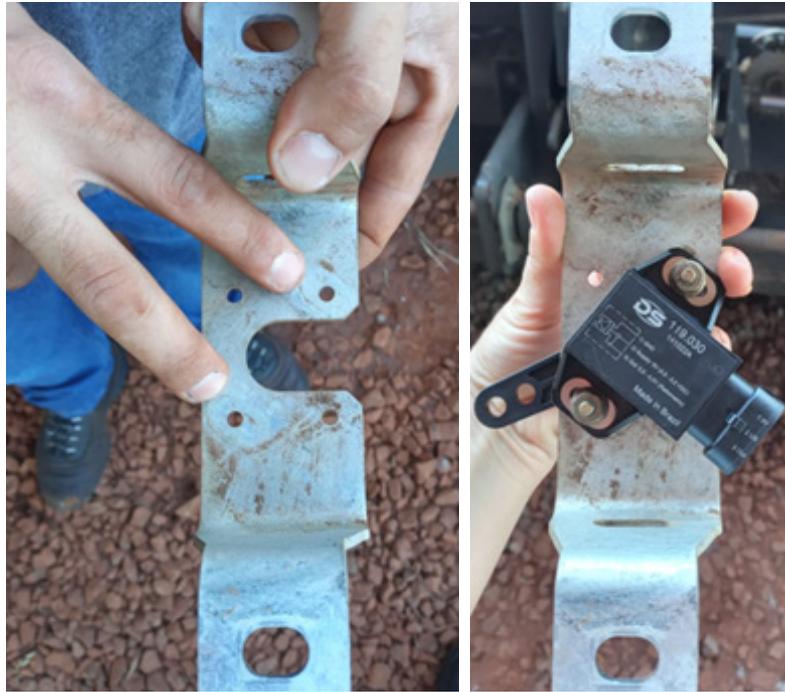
Pinagem eletrônica do sensor DS-119.030
